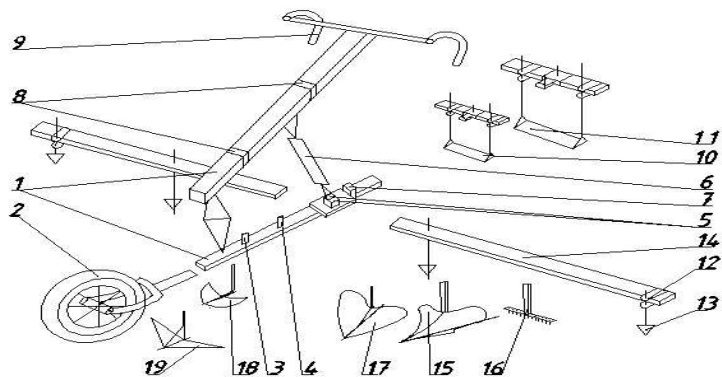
Складові деталі універсального пристрою для обробки присадибної ділянки. 1 – рама; 2 – колесо; 3,4,8 – твори; 5,7 – гнізда; 6 – регулювальна тяга; 9 – рукоятки; 10,11 – ножі; 12 – хомут; 13 – центральна лапа маркера; 14 – штанги; 15 – підгортальник; 16 – граблів; 17 – плужок; 18 – перепідгортальник; 19 – плоскоріз;
